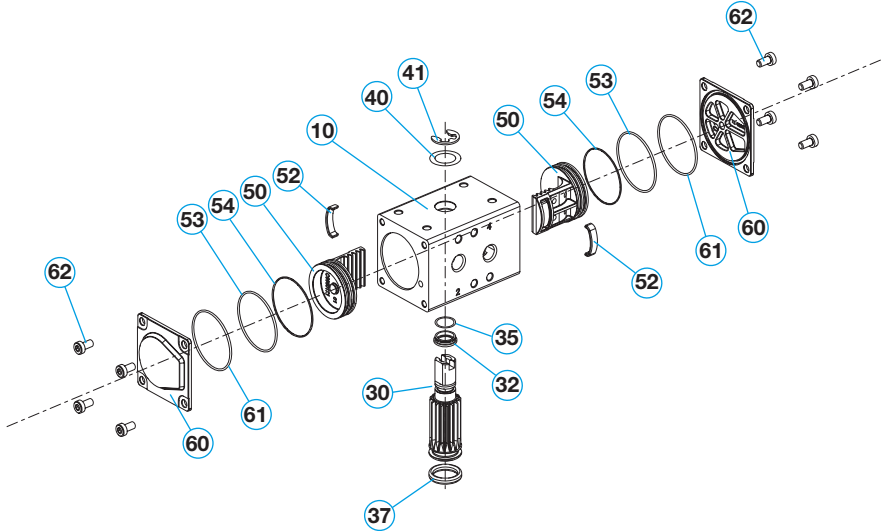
Explosionszeichnung aller Einzelkomponenten Schwenkantrieb actubar
